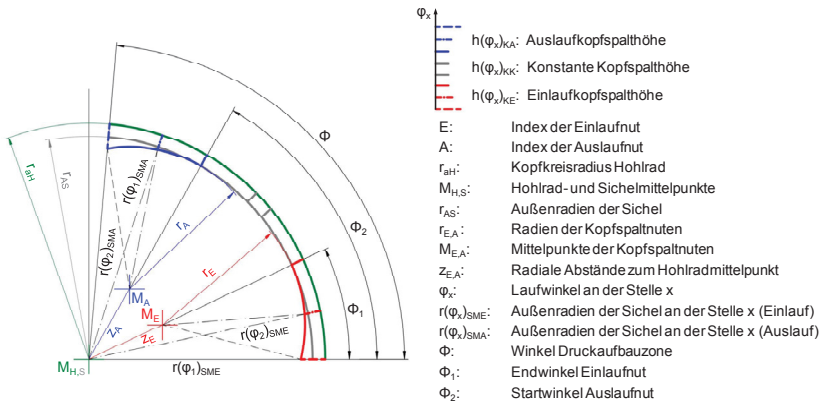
Ausgleichsnuten im Gehäuse
